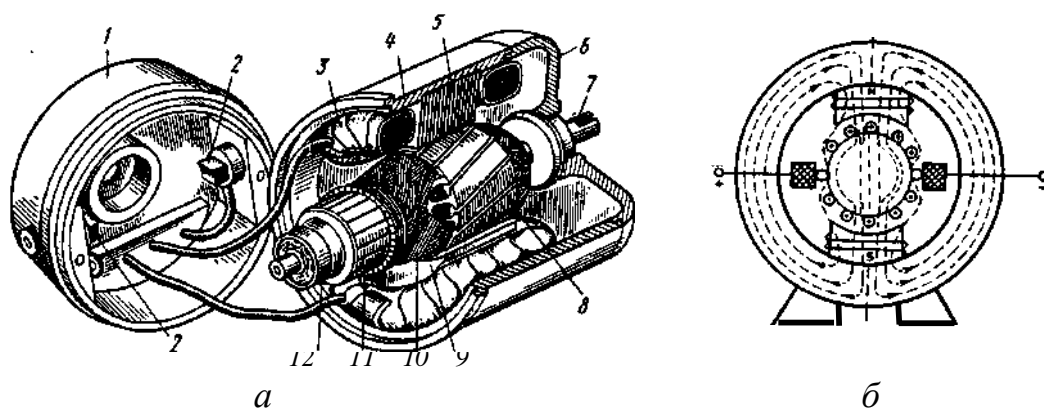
Внешний вид конструкции и схематическое устройство двигателя постоянного тока
